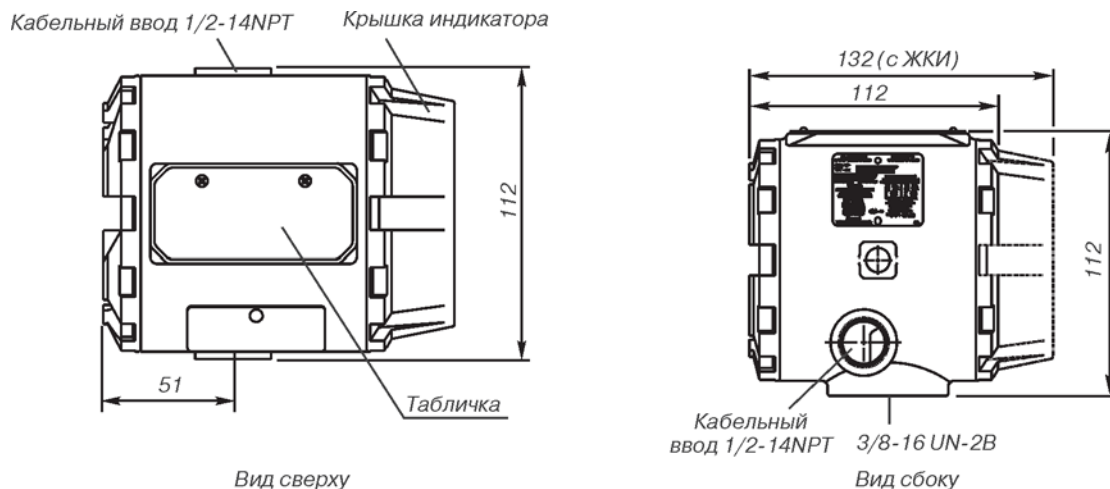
Габаритный чертеж преобразователя. Кабельный ввод 1/4-NPT*.
